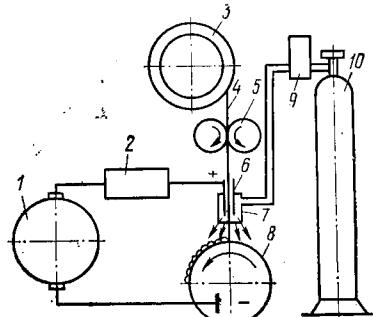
Схема установки для автоматической наплавки в углекислом газе
